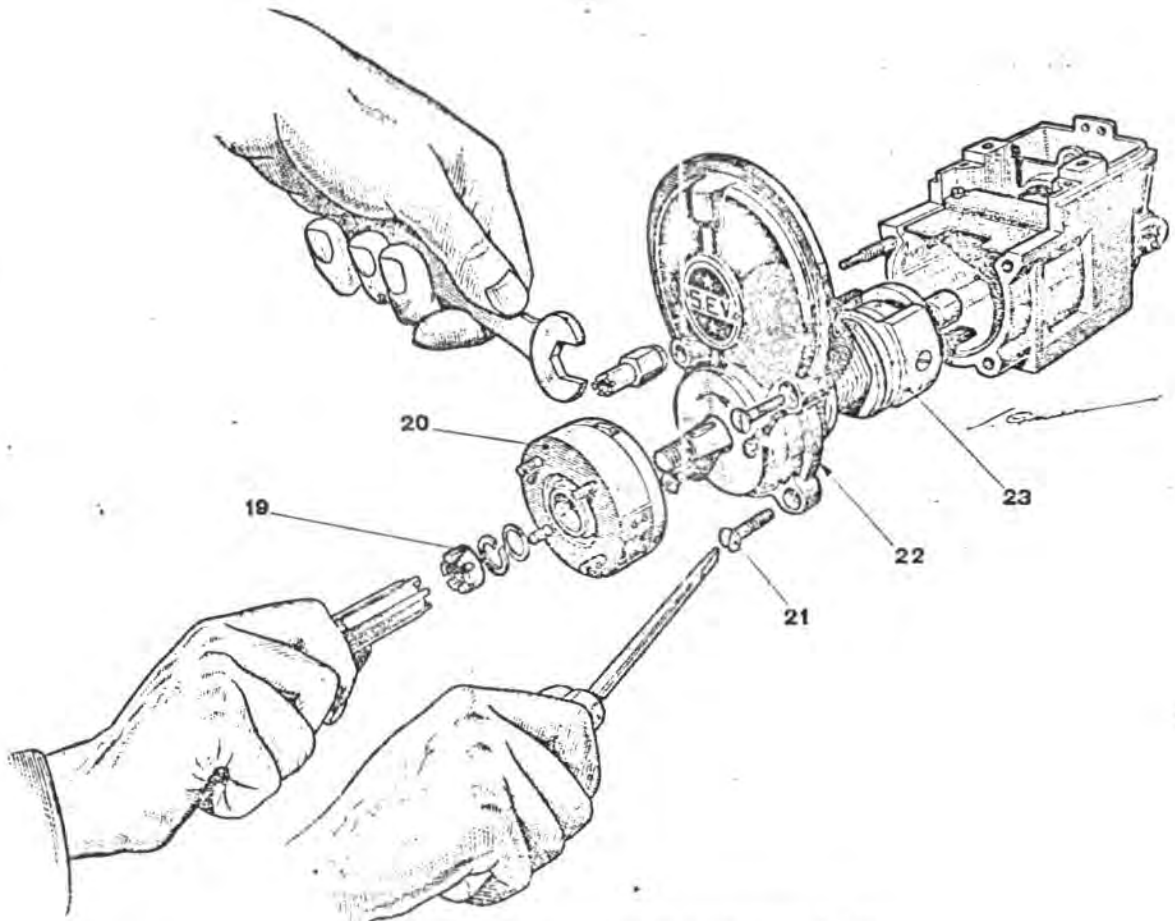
DÉMONTAGE DU DÉLIC ET DU FLAQUE AVANT
